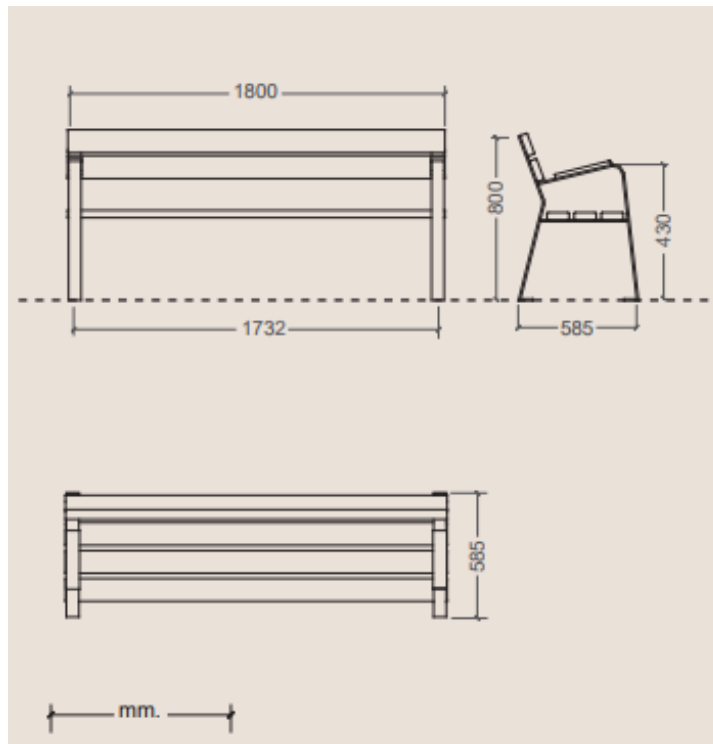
Detalle de alzado, perfil y planta del banco. (Fuente: Mobipark).
